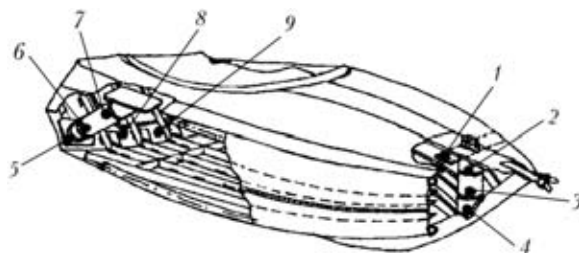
Расположение характерных повреждений ТК: 1 — усиление носовой лебедки; 2–4 — разрушения носовой стойки; 5–7 — места разрушения кормовой стойки; 8, 9 — усиление кормы под двигателем
